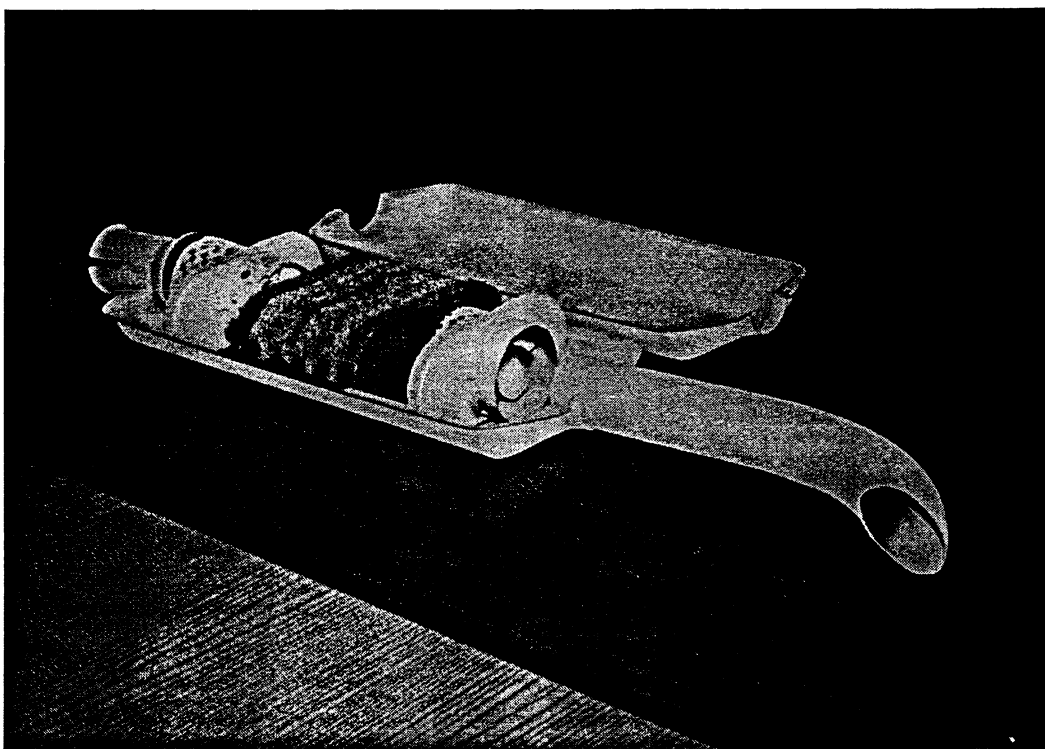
Нейтрализатор, изготовленный на базе глушителя 60-1205015-А(ММЗ)
